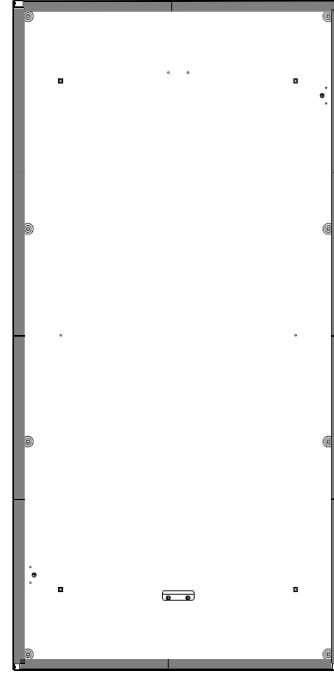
Detalles de colocación de las placas cubretornillos instaladas en las placas superior e inferior del gabinete I-Line™.
